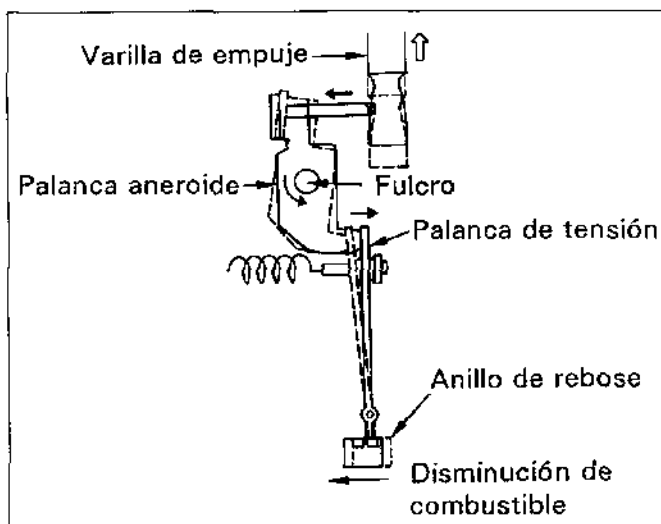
Cuando la presión de refuerzo es baja (en elevación alta)
